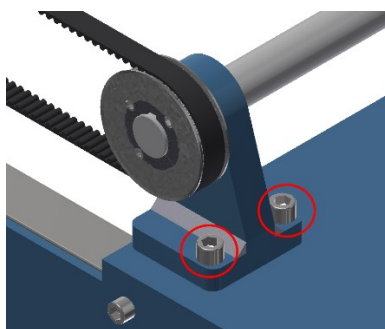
Pojezdová rolna s přírubou a deska pro upnutí řemenu
